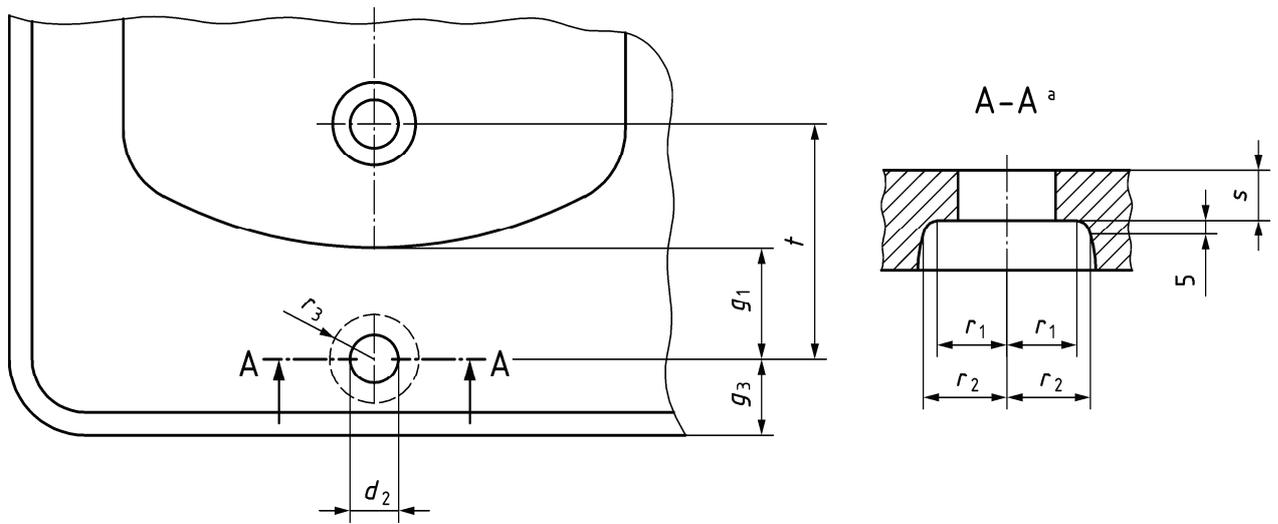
Anschlussmaße für Waschbecken mit einem zentralen Armaturenloch
